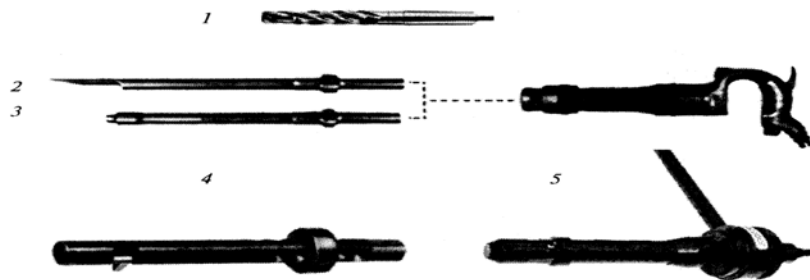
Инструмент для извлечения труб из гнёзд трубных решёток: 1-ступенчатое сверло; 2,3-зубило и выколотка с пневмомолотком; 4,5-труборезы
